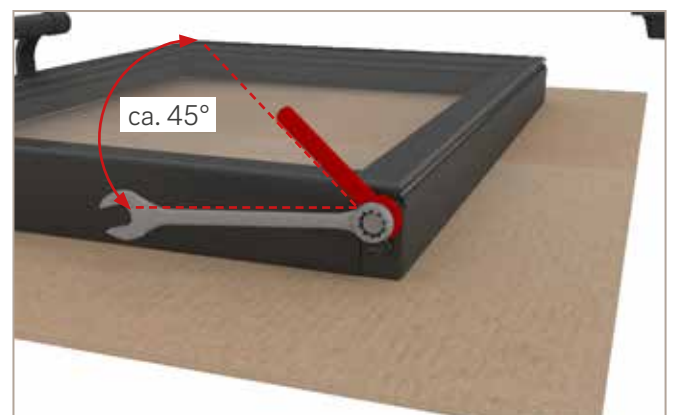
Türfeder mit Spannschlüssel vorspannen
